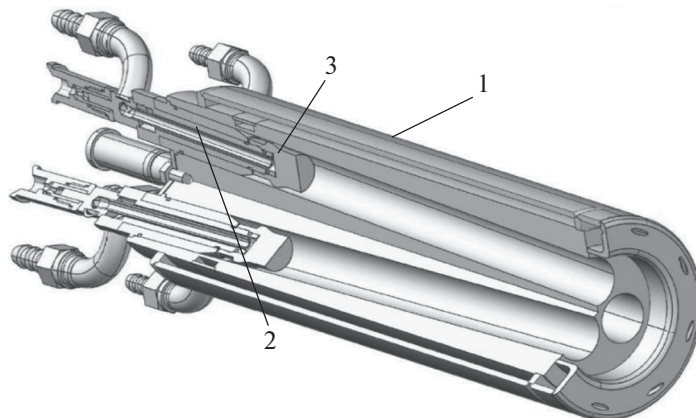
Высоковольтный трехфазный плазмотрон переменного тока: 1 — корпус, 2 — изолятор, 3 — электрод.
